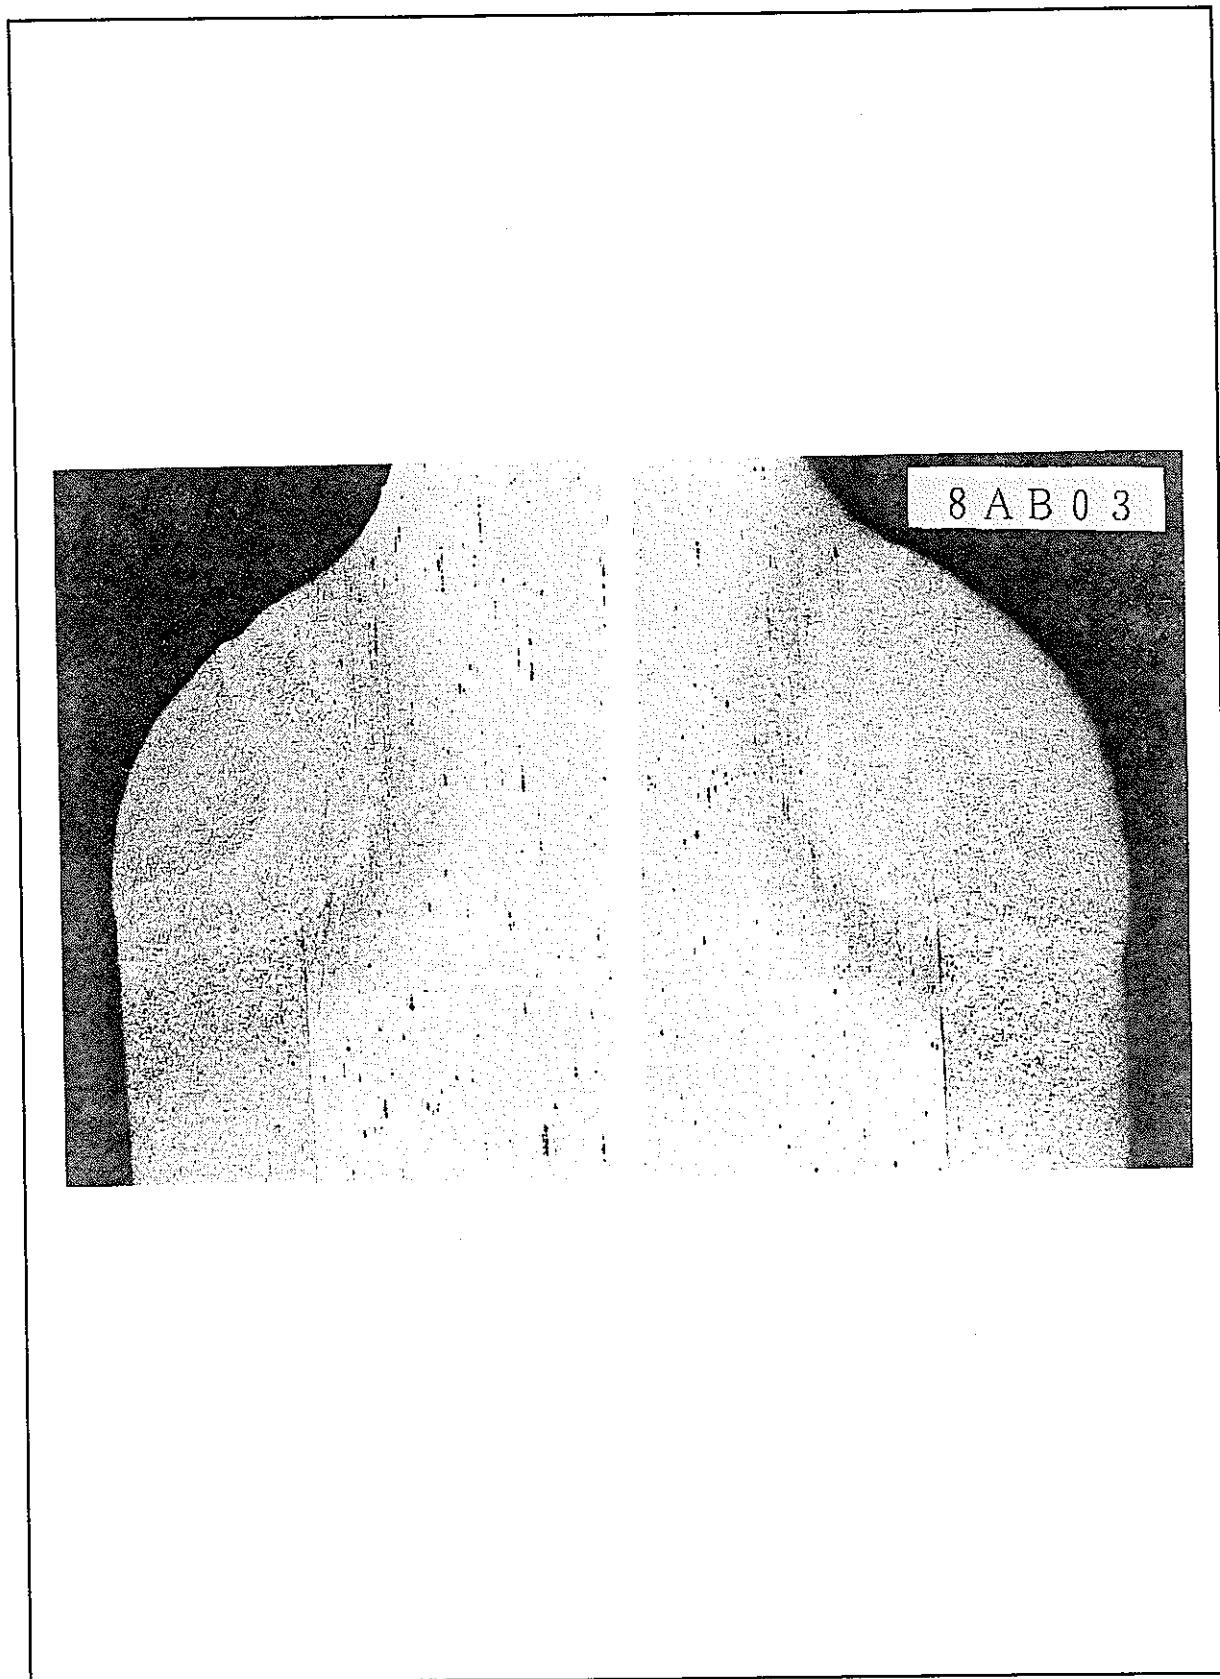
下部端栓溶接施行断面金相写真 (HT 9M)
